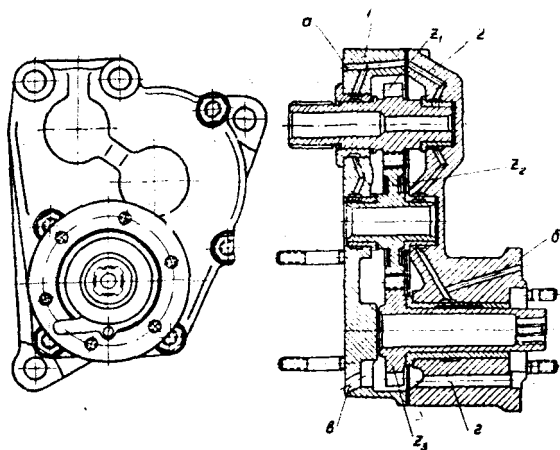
Привод компрессора АК-50М; 1—корпус; 2—крышка; а—входной масляный канал; б—канал подвода масла к компрессору; Z_1 —ведущая шестерня; Z_2 —промежуточная шестерня; Z_3 —ведомая шестерня
